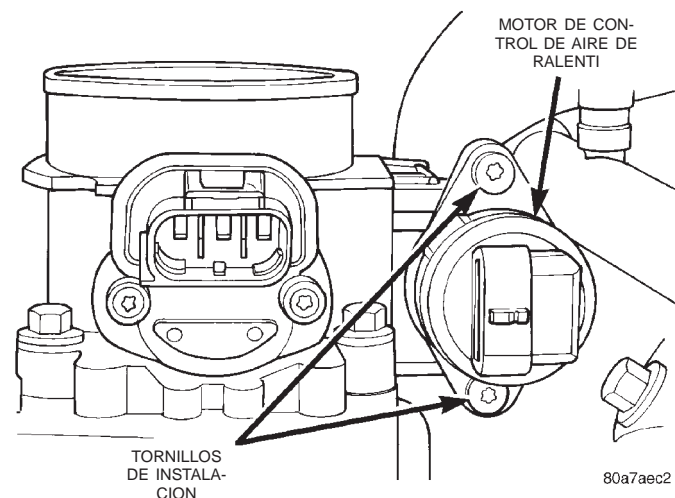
Pernos de instalación (tornillos)—Motor de IAC
